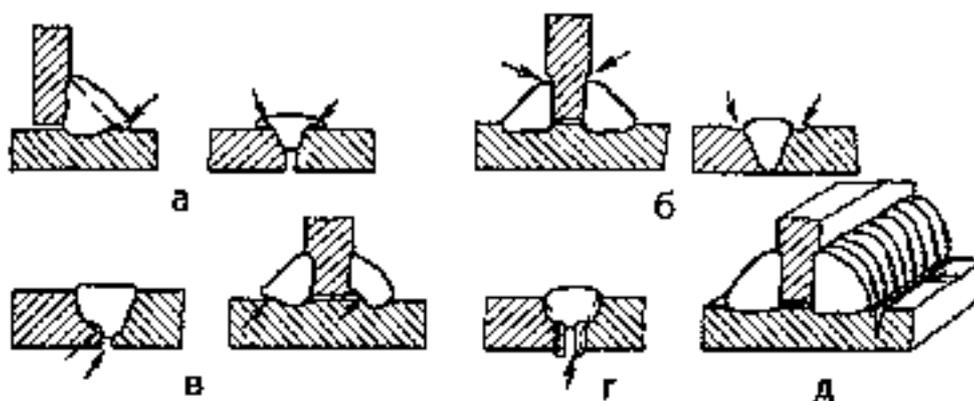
Наружные дефекты сварного шва:
